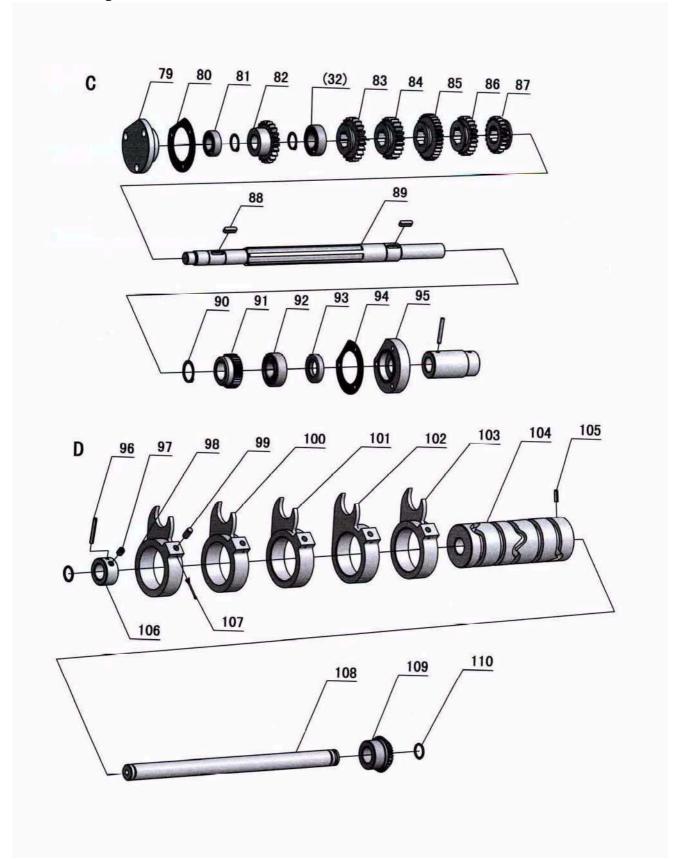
Vorschubgetriebe 3 von 4 - Headstock feed gear 3 of 4
